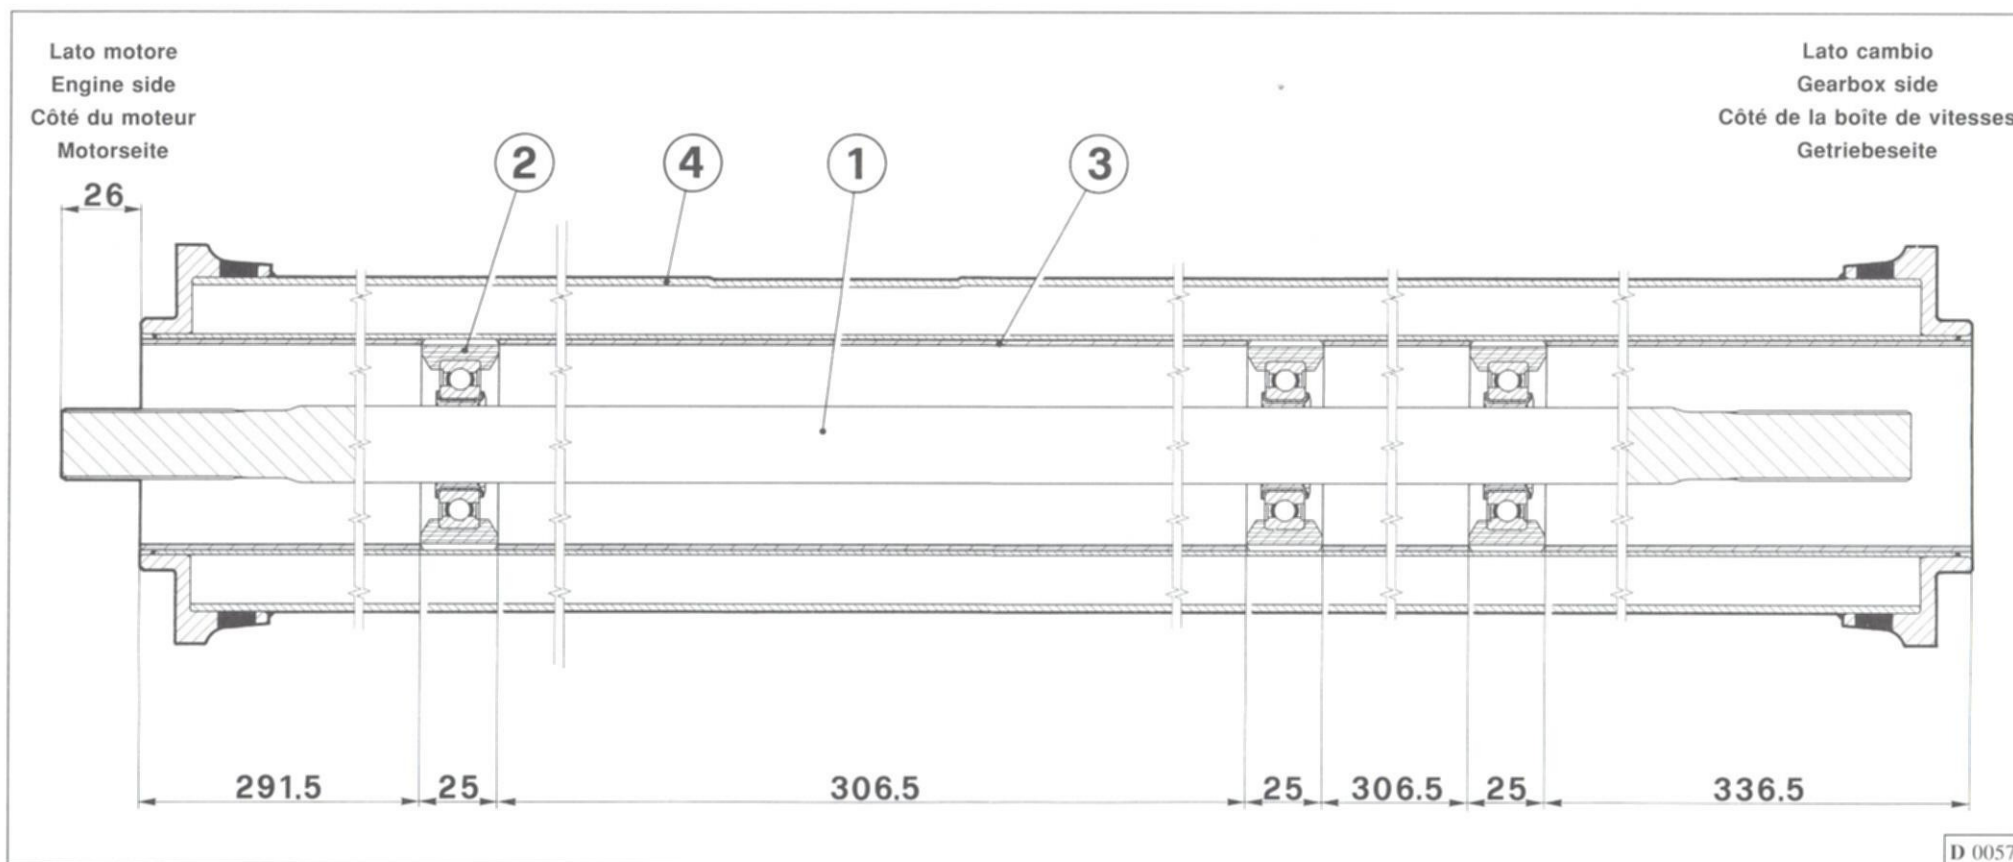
Complessivo del tubo di collegamento motore-cambio
